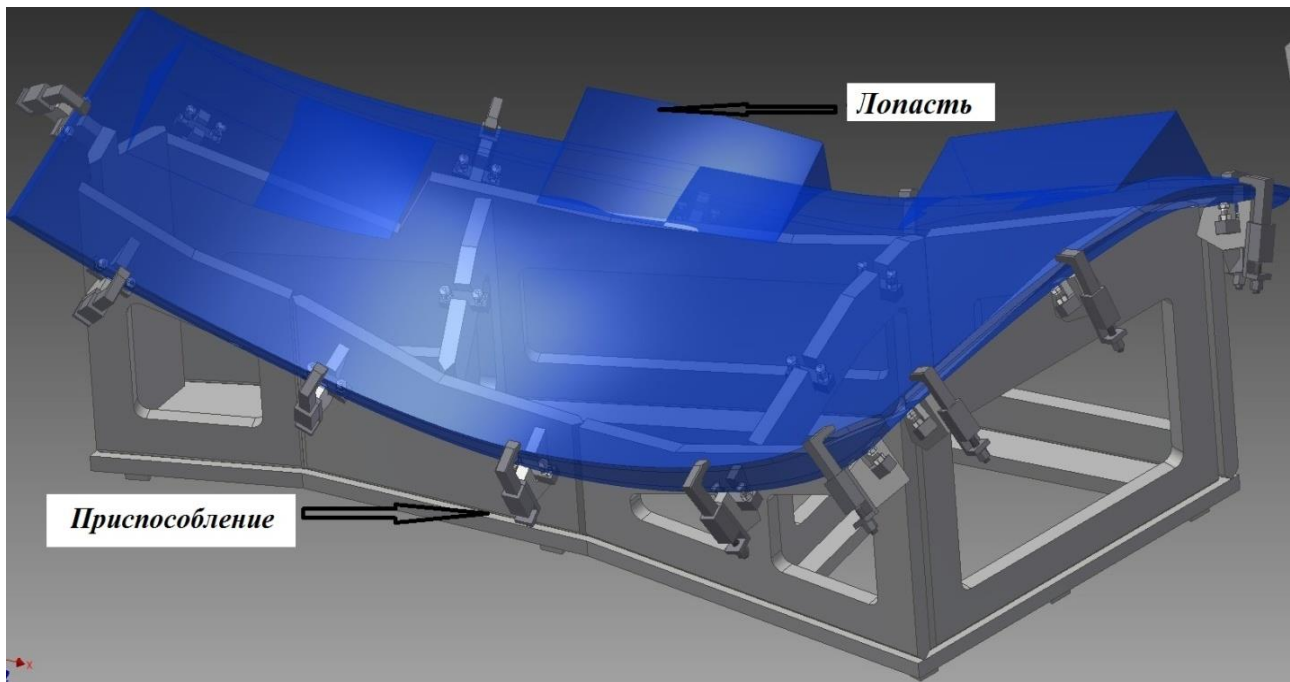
Приспособление для фрезерования «рабочей» стороны лопасти
